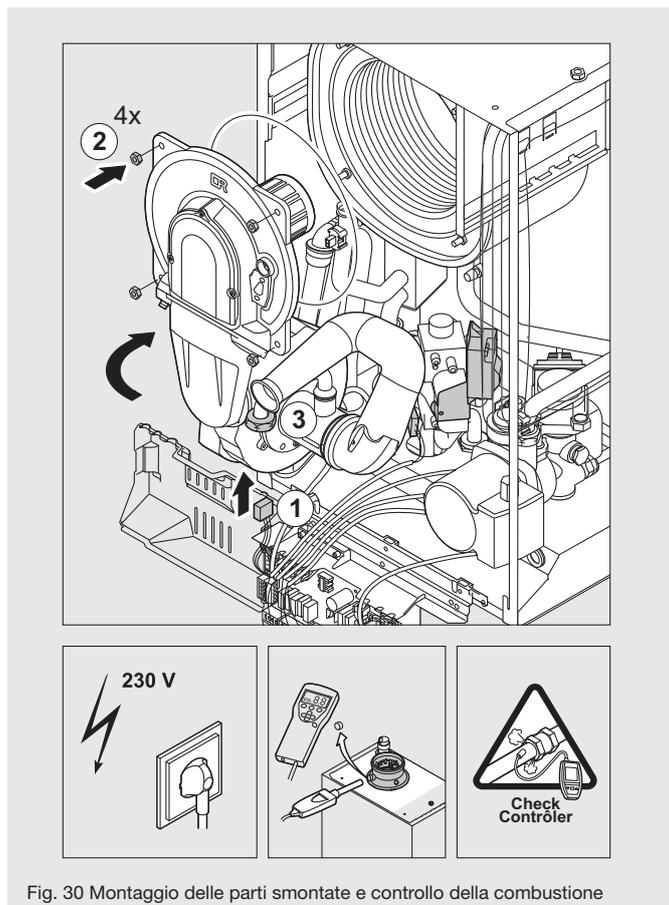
Montaggio delle parti smontate e controllo della combustione
